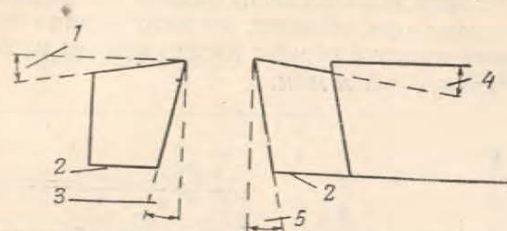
Заточка резцов для обработки нержавеющих сталей:
